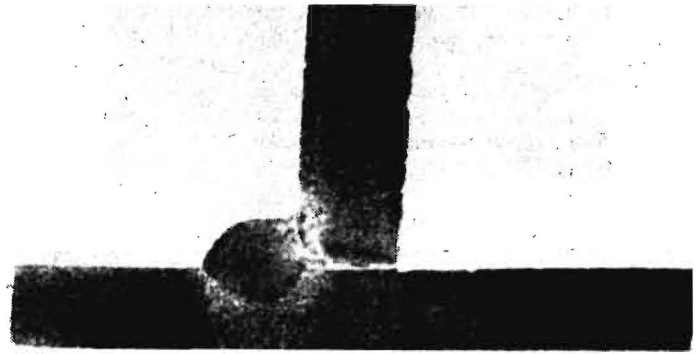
Schweißnahtfehler der Gruppen D und F nach Standard TGL 10646
